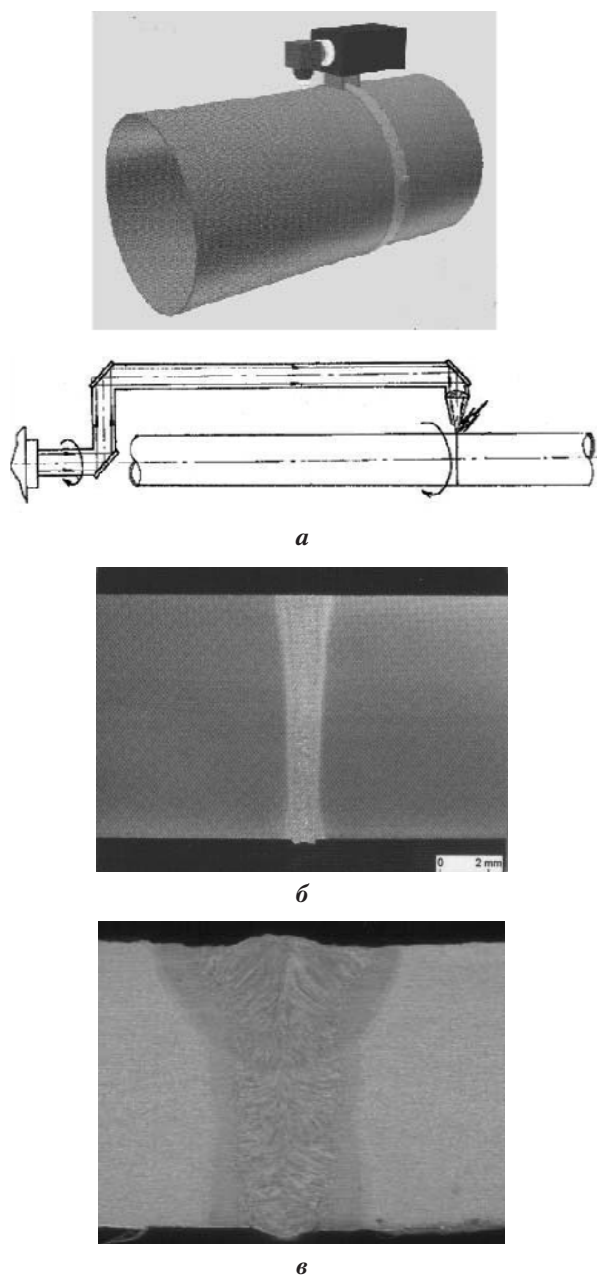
Лазерная сварка кольцевых швов магистральных трубопроводов: *а* – схемы орбитальной сварки; *б* – макроструктура шва, полученного однопроводной лазерной сваркой; *в* – макроструктура шва, полученного четырехпроводной лазерно-дуговой сваркой
